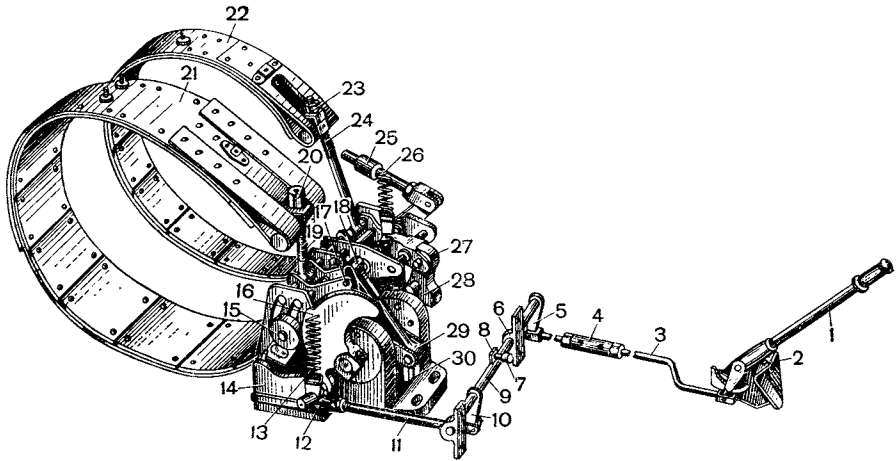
Тормозные ленты и привод управления планетарным механизмом поворота (левый):
